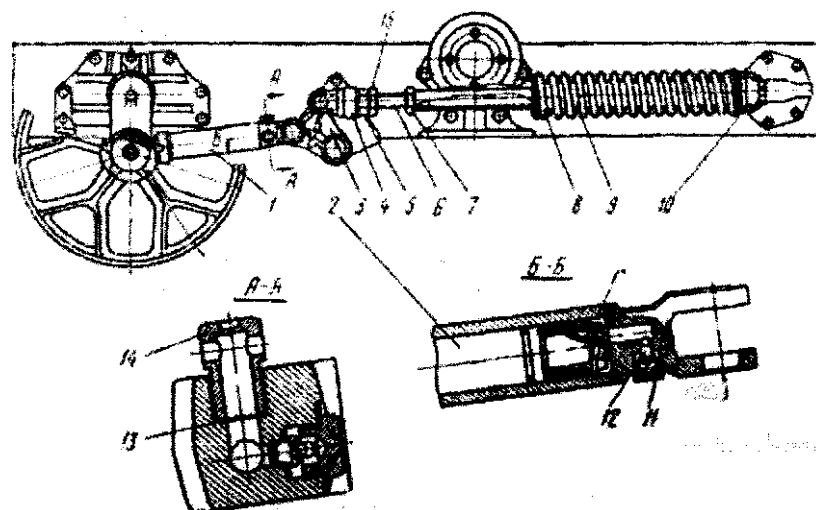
Напрявне колесо з натяжним і амортизаційним пристроями: 1 - циліндр гідронатягу гусениць; 2 - шток; 3 - ланка проміжна; 4 - вилка; 5 - гайка; 6 - болт натяжний; 7 - гайка; 8 - пружина велика; 9 - пружина мала; 10 - опора кульова; 11 - пробка; 12 - оливниця; 13 - клапан пластинчатий; 14 - корпус клапана; 15 – контргайка.
